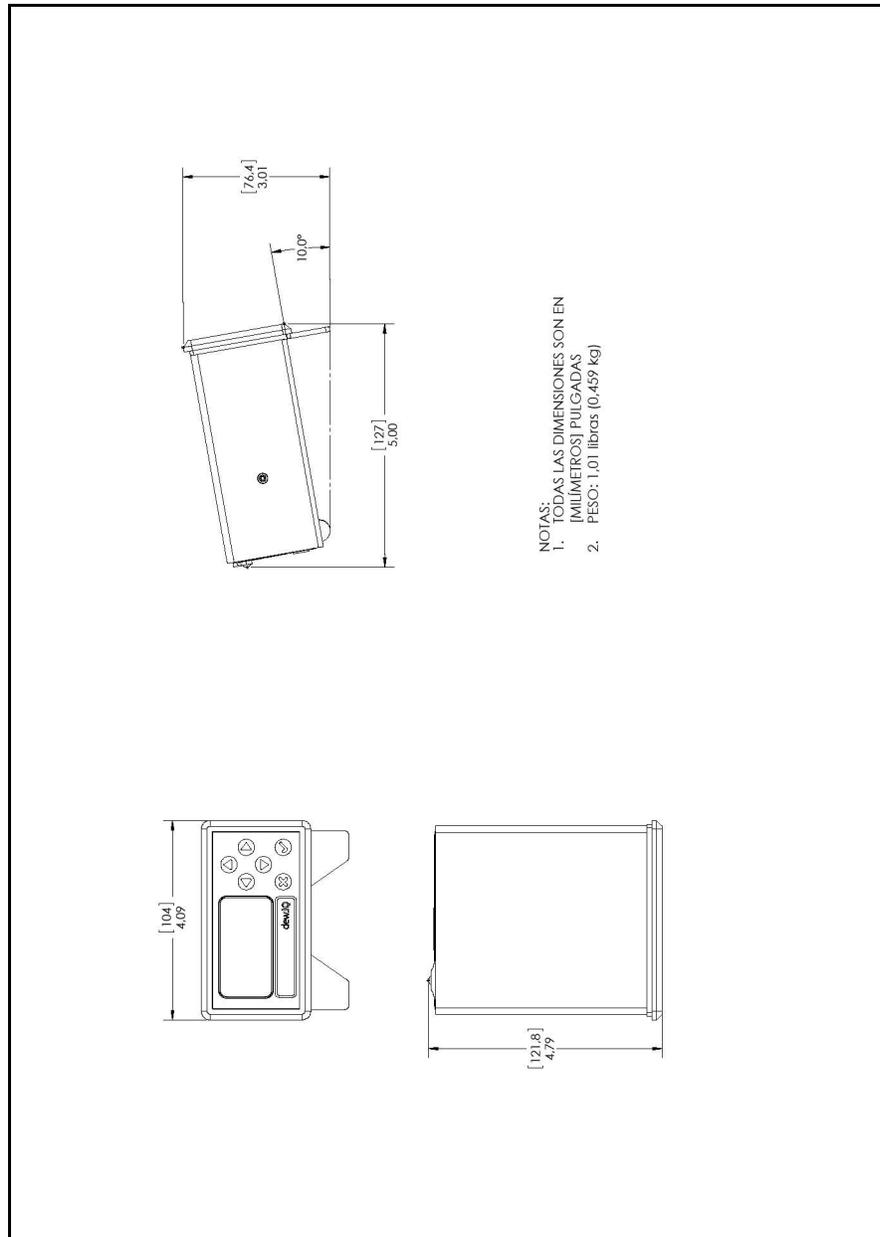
Croquis y plano de instalación en mesa de trabajo (plano de referencia 712-1826)
